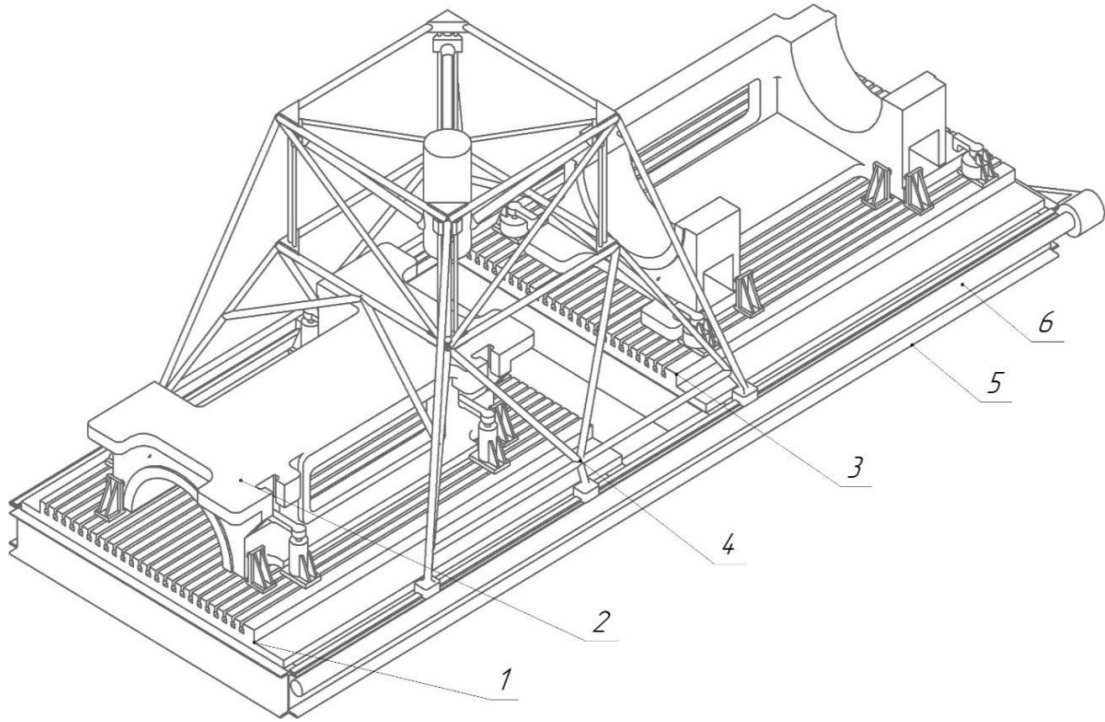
Технологічна машина для обробки корпусних деталей:
